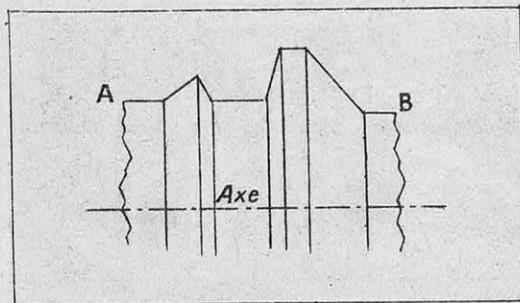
PIÈCE PROFILÉE DE RÉVOLUTION QUE L'ON PEUT FABRIQUER EN GRANDE SÉRIE PAR LA MÉTHODE DU MEULAGE AVEC « CRUSHING ROLL »
